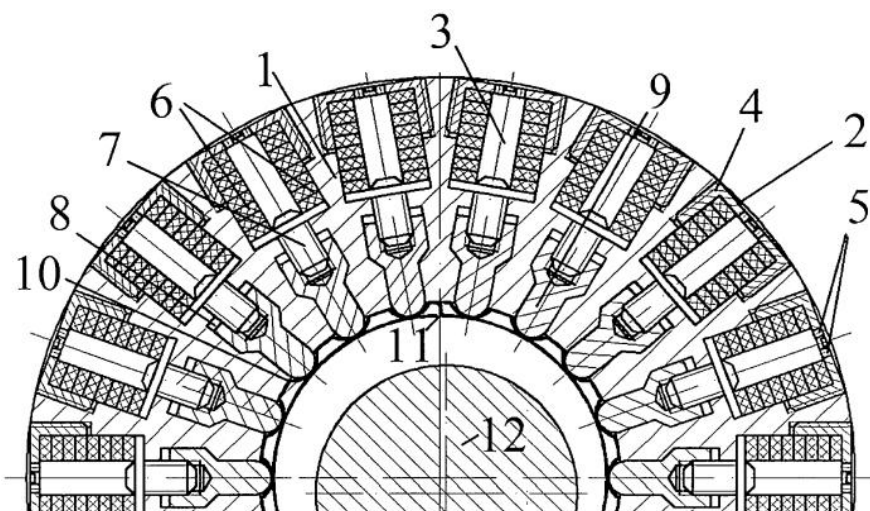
Лепестковый газодинамический подшипник с активным управлением
